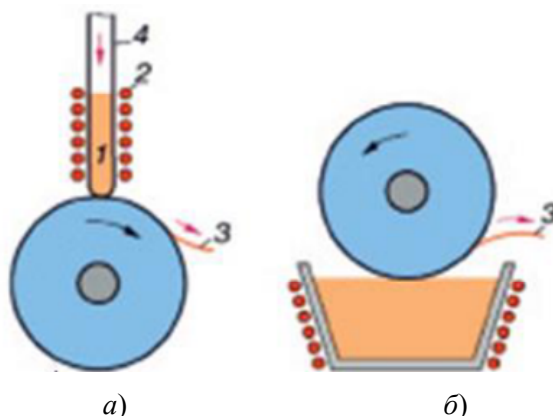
Схемы устройств для получения аморфных сплавов закалкой из жидкого состояния: а – нанесение расплава на вращающийся металлический диск или цилиндр; б – извлечение расплава вращающимся диском; 1 – расплав; 2 – нагревательное устройство (индукционная печь); 3 – лента аморфного сплава; кварцевая трубка
